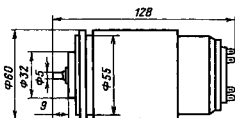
27 Габаритные и установочные размеры двигатель-генератора АДГ-607А
